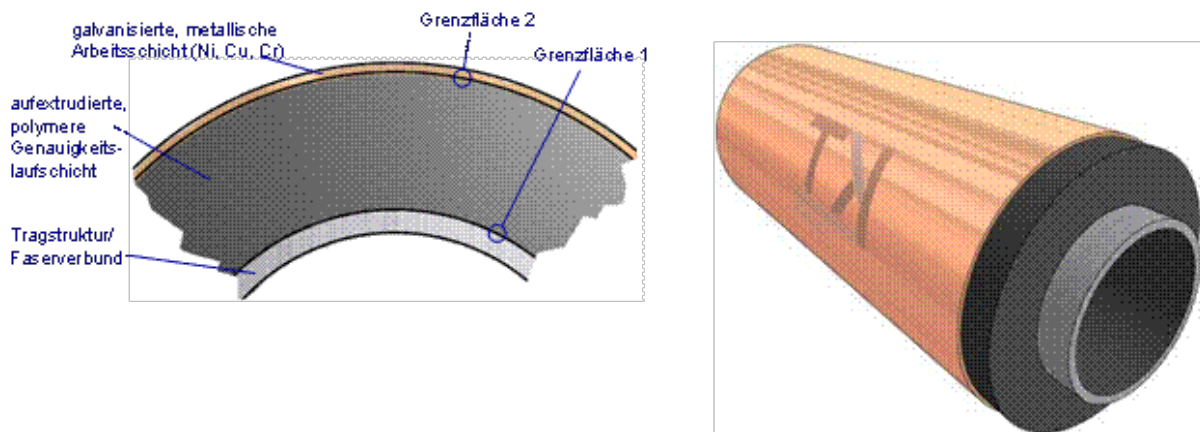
prinzipieller Aufbau des formatvariablen Druckzylinders
